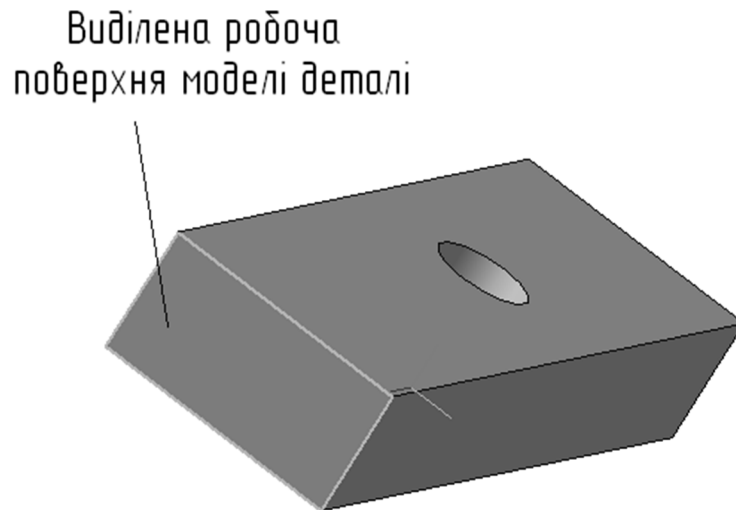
Приклад виділення поверхні деталі, на якій необхідно створити інший формоутворювальний елемент
